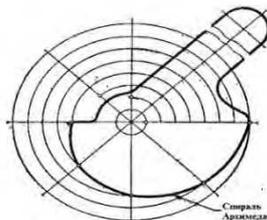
Контур эксцентриковой рукоятки приспособления для зажима деталей, выполненный с помощью спирали
